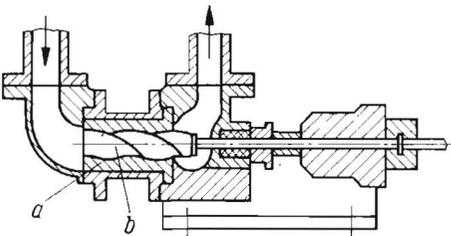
Schraubepumpe (Einspindelpumpe) mit Gummistator a Stator, b Spindel
